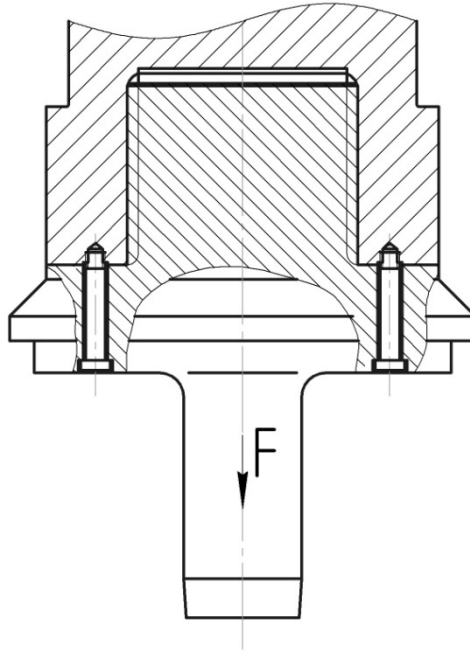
Розрахункова схема групового болтового з'єднання
